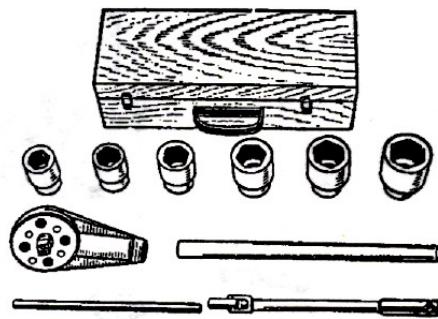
Редуктор-усилитель крутящего момента с набором торцовых ключей
